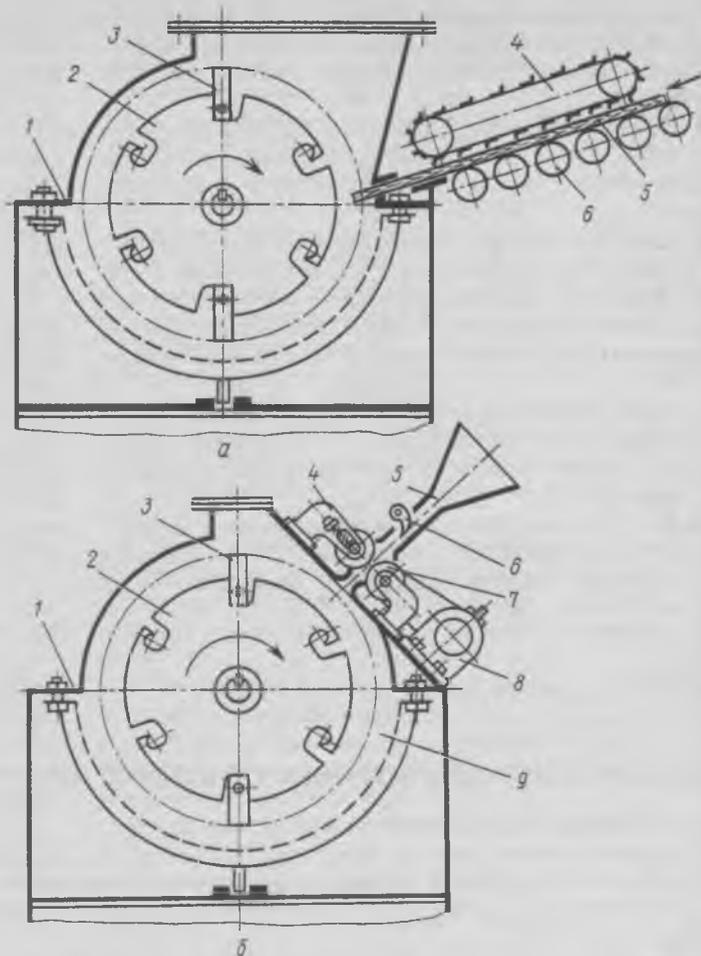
Установка для измельчения кусковых древесных отходов на базе дробилки ДМ-7:
